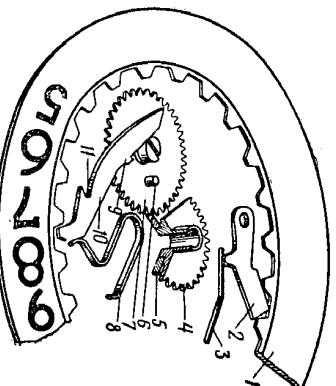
Кинематическая схема календарного устройства часов «Полет» 2616:
